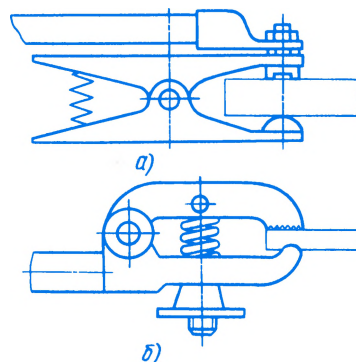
Зажимы для присоединения сварочного провода к свариваемому изделию:
